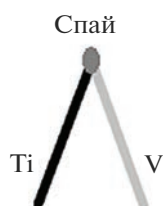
Вид исходного образца после аргоновой сварки.
